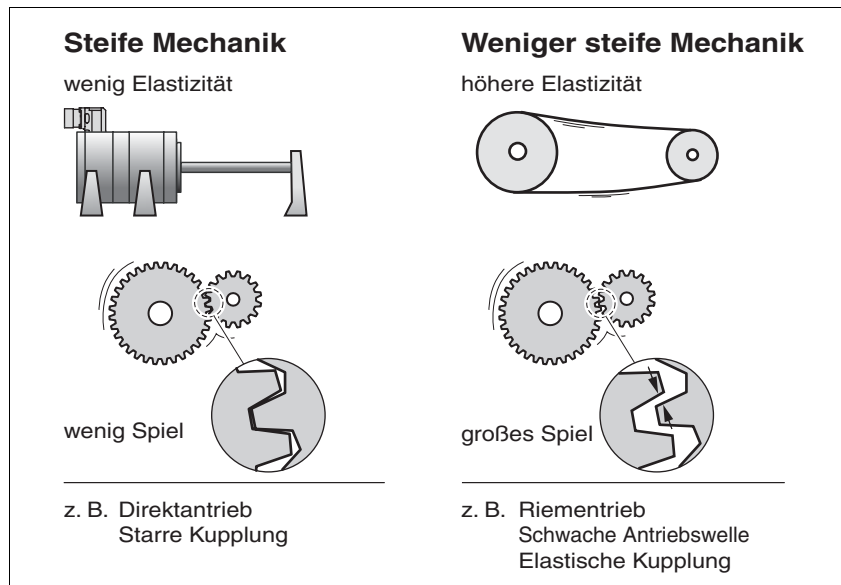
Mechanische Systeme mit steifer und weniger steifer Mechanik
